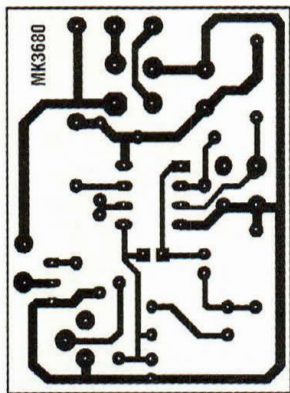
Reproduction du circuit imprimé à l'échelle 1 vu côté soudures.
